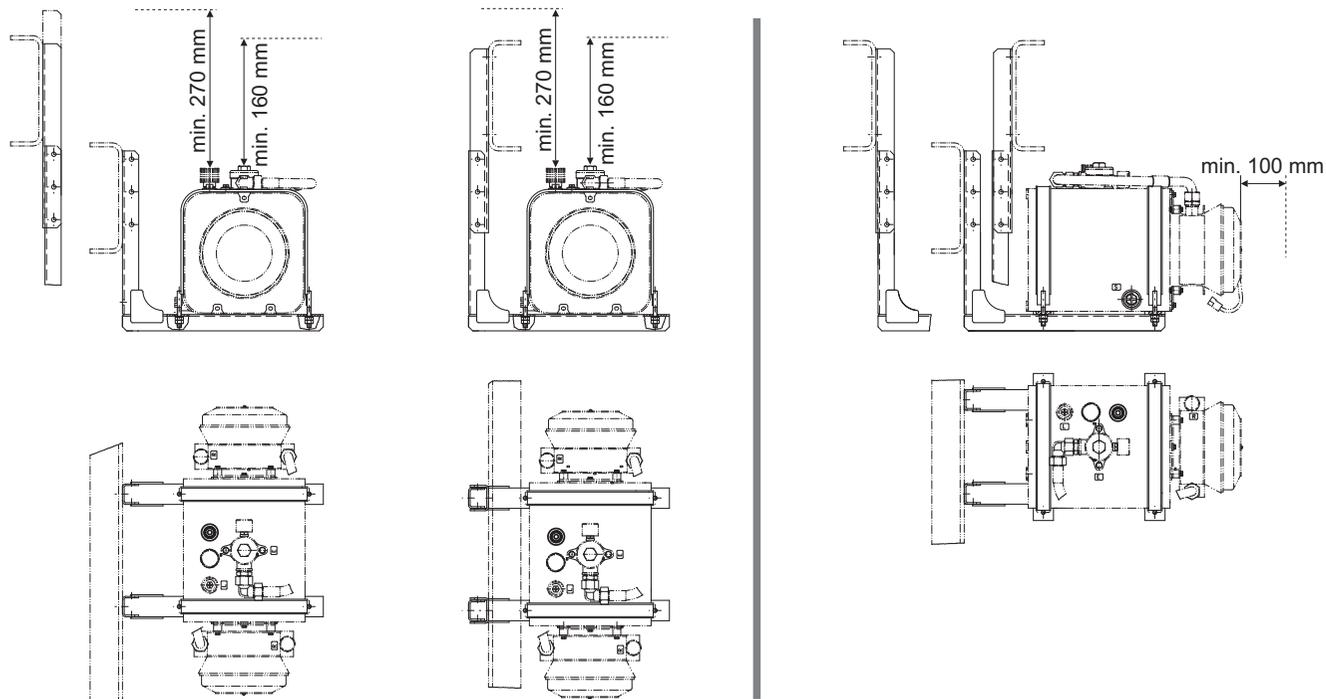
Befestigung des Öltanks innen oder außen und längs bzw. quer am Fahrzeugrahmen
